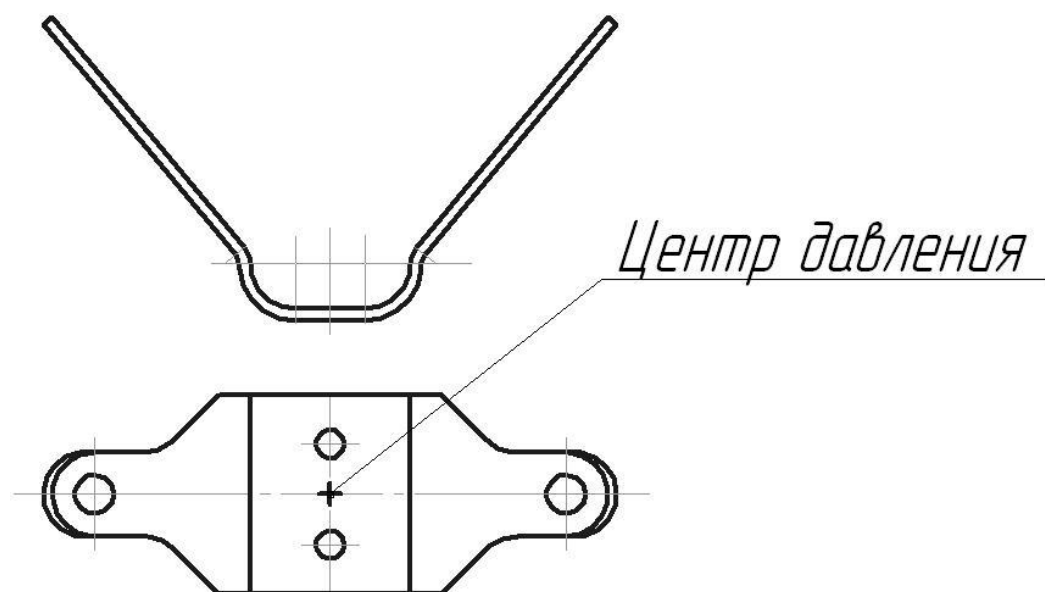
Расположение центра давления штампа детали «скоба».
